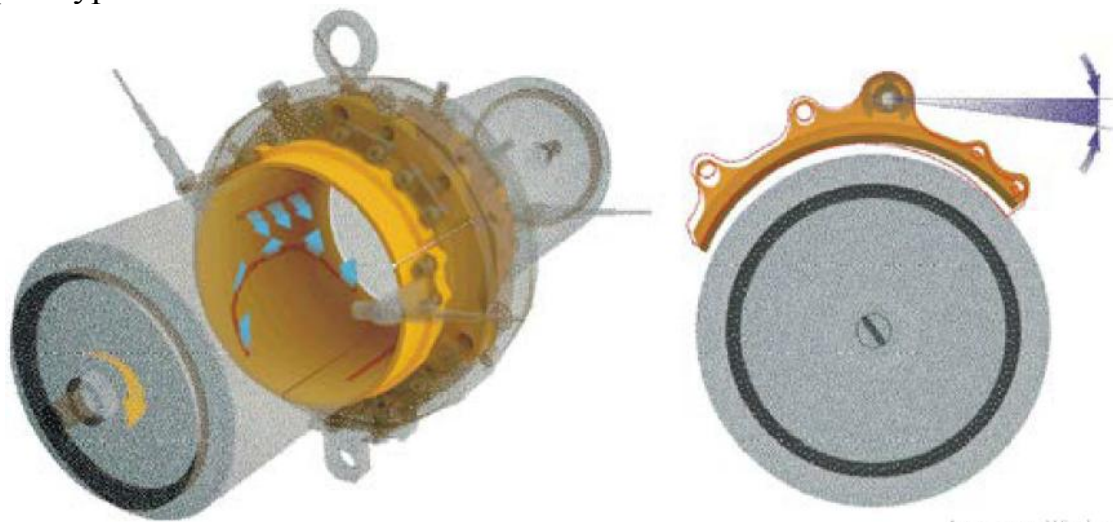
Конструкция гибридного подшипника с вращающимися вставками [3].
